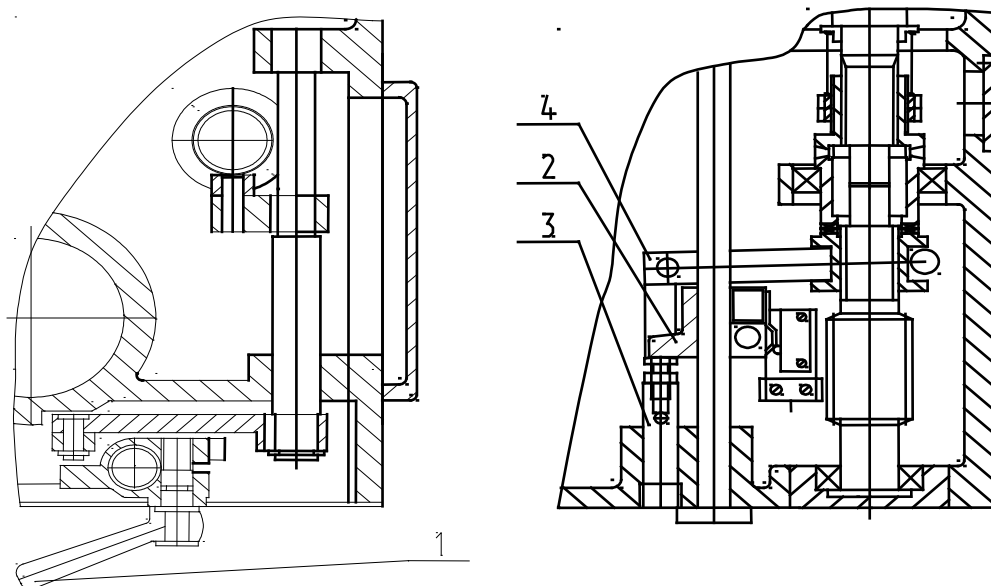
Механизм включения реверса шпинделя при резьбонарезании и механизм автоматического отключения подачи при сверлении
